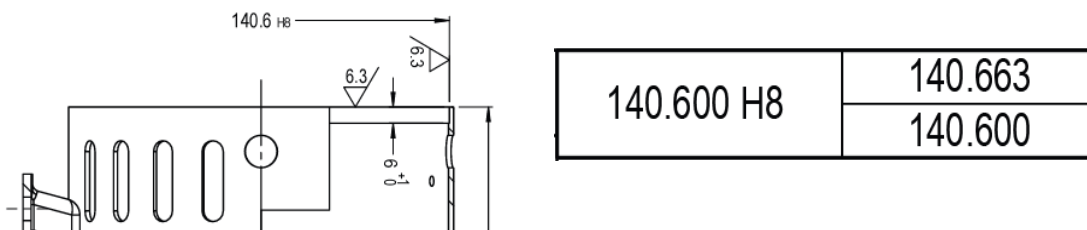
Tolerancias de maquinado de guías en carcasa.
